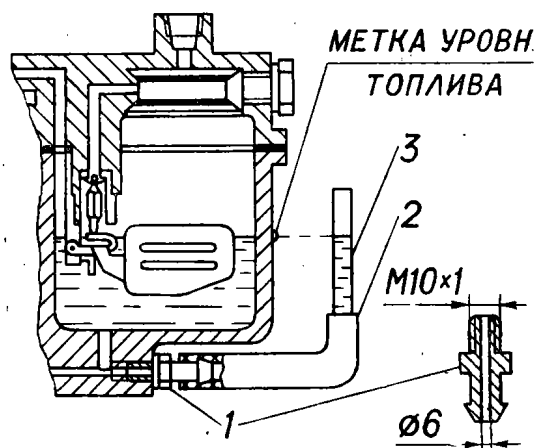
Схема проверки уровня топлива в поплавковой камере:
